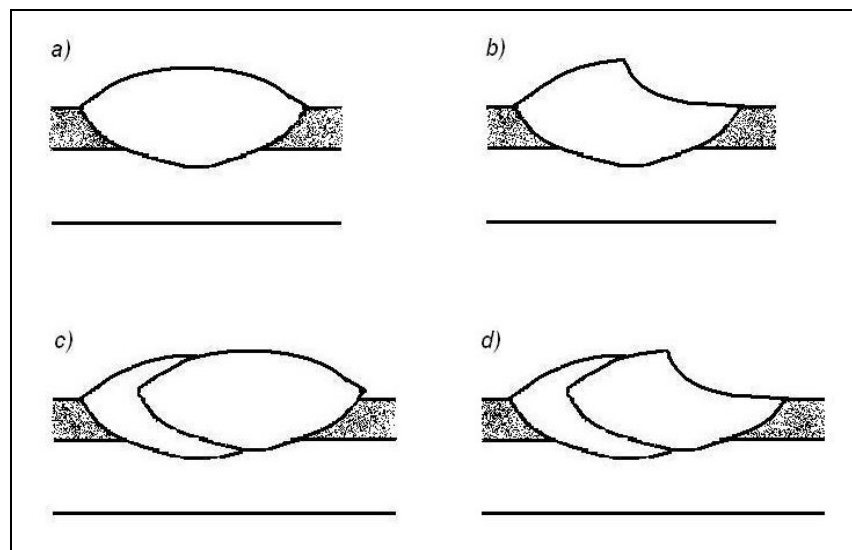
Representação esquemática da seqüência de operações para revestimento com retirada parcial dos cordões de solda. a) deposição do primeiro cordão; b) esmerilhamento do primeiro cordão; c) deposição do segundo cordão; d) esmerilhamento do segundo cordão para deposição do próximo.
